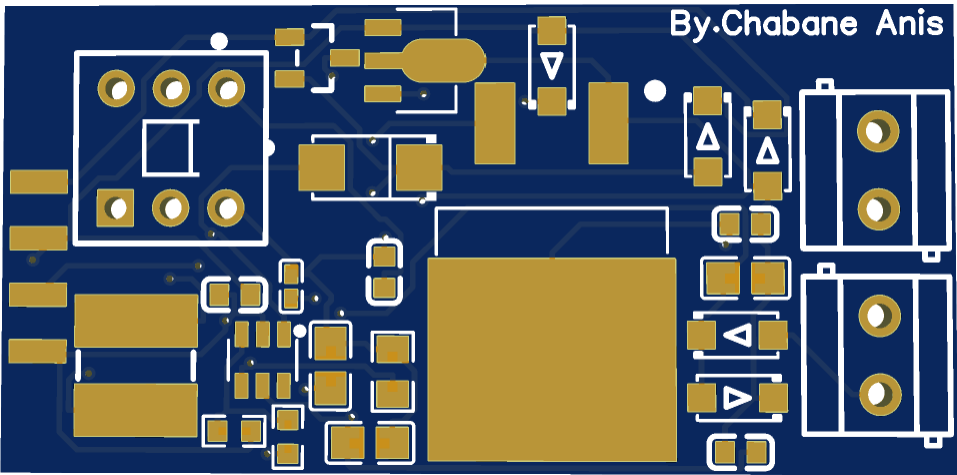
Vue de dessus de la disposition du PCB d'alimentations sans composants
